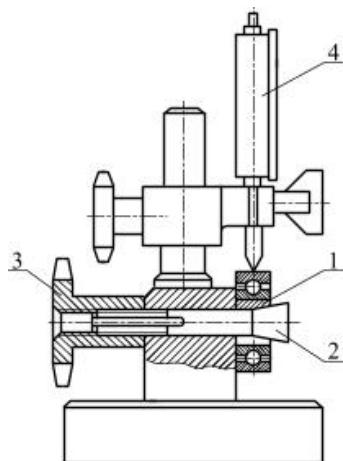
Пристрій для контролю радіального зазору підшипника: 1 – розрізна втулка; 2 – конусна оправка; 3 – гайка; 4 – індикатор
